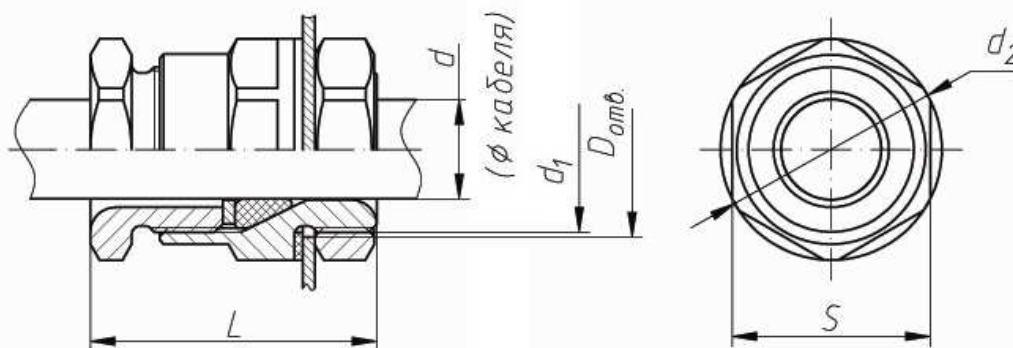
Кабельный ввод для открытой прокладки кабеля (тип К)
